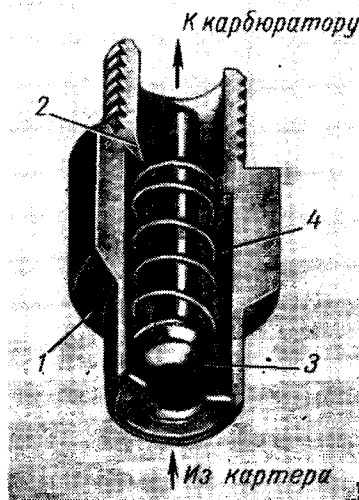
Самоочищающийся клапан системы принудительной вентиляции картера: 1 — корпус; 2 — отверстие; 3 — плунжер; 4 — пружина.
